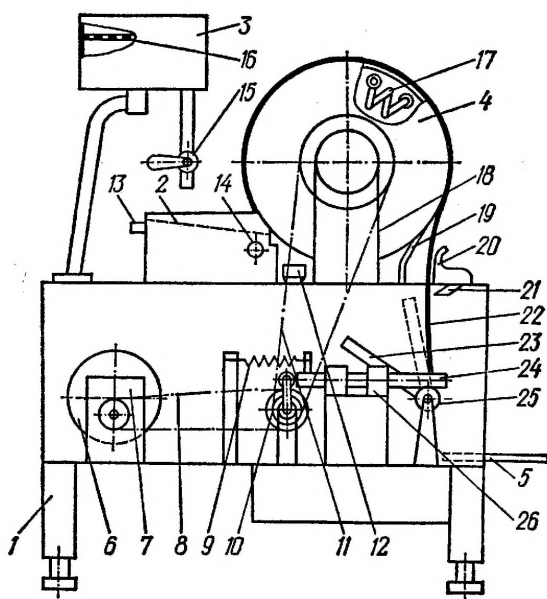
Схема жаровні електричної з барабаном, що обертається, ВЖШЭ-675: 1 – рама; 2 – приймальний лоток; 3 – бачок для тіста; 4 – жарильний барабан; 5 – металевий лист; 6 – електродвигун; 7 – черв'ячний редуктор; 8 – ланцюгова передача; 9 – пружина; 10 – ролик; 11 – ланцюгова передача; 12 – коритоподібний піддон; 13 – патрубок для шлангу подачі води; 14 – зливний патрубок; 15 – кран; 16 – сітка-фільтр; 17 – ТЕН; 18 – кронштейн; 19 – скребковий ніж; 20 – напрямні; 21 – відрізний ніж; 22 – млинна стрічка; 23 – відсікач; 24 – зубчата рейка; 25 – підшипники
